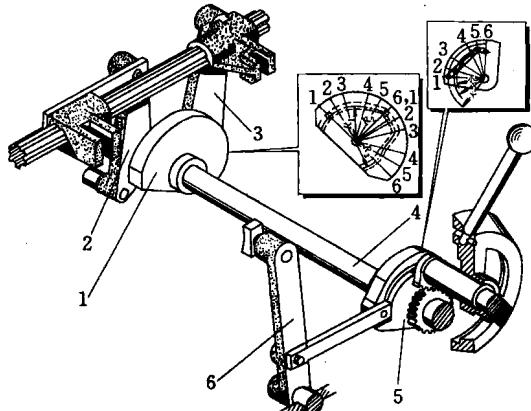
轴Ⅳ及轴Ⅵ上滑动齿轮的操纵机构
